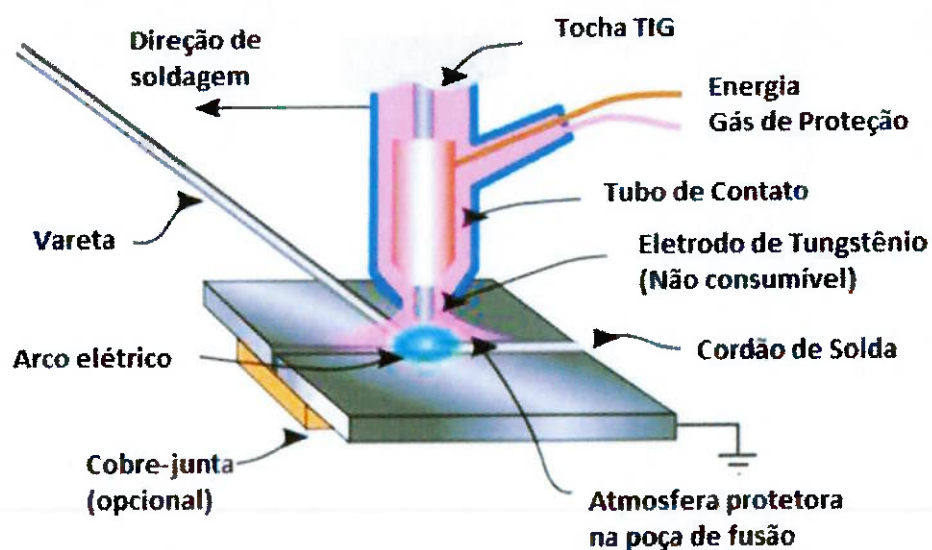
11 - Processo de soldagem TIG [Adaptado da referência] [1]
